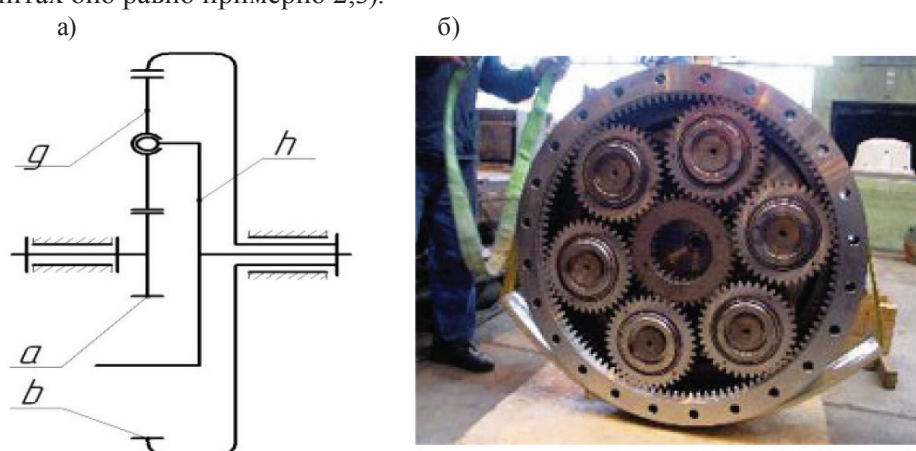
Планетарный механизм $2kh$ типа A : а — принципиальная схема механизма; б — шестисателлитный механизм выходной ступени редуктора привода лебедки для установки якорей (Норвегия)
